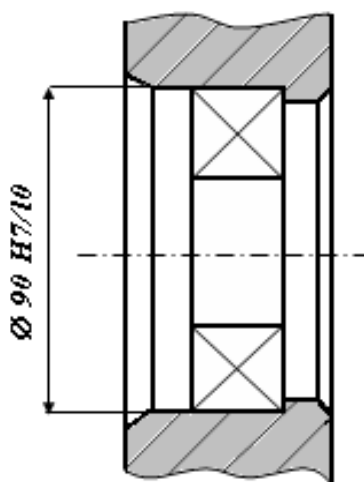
Обозначение посадки наружного кольца подшипника в корпус
